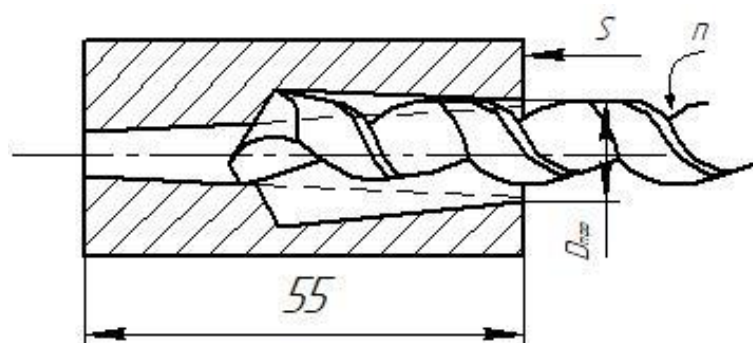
Схема процесса образования отверстия с обратной конусностью
